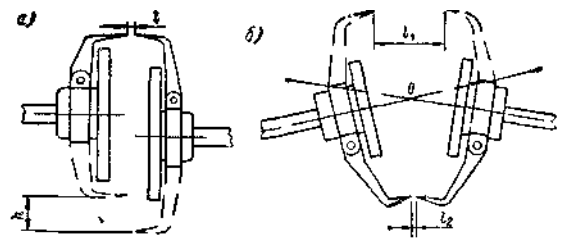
Определение неточности установки гребного вала; а — смещение осей; б — излом линии вала.
